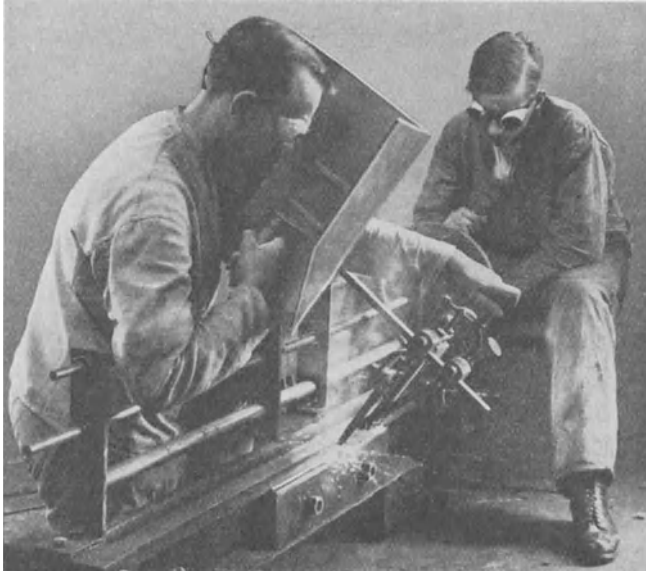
Ausführung einer Schweißnaht am Schienenkopf unter Benutzung einer Führung.
